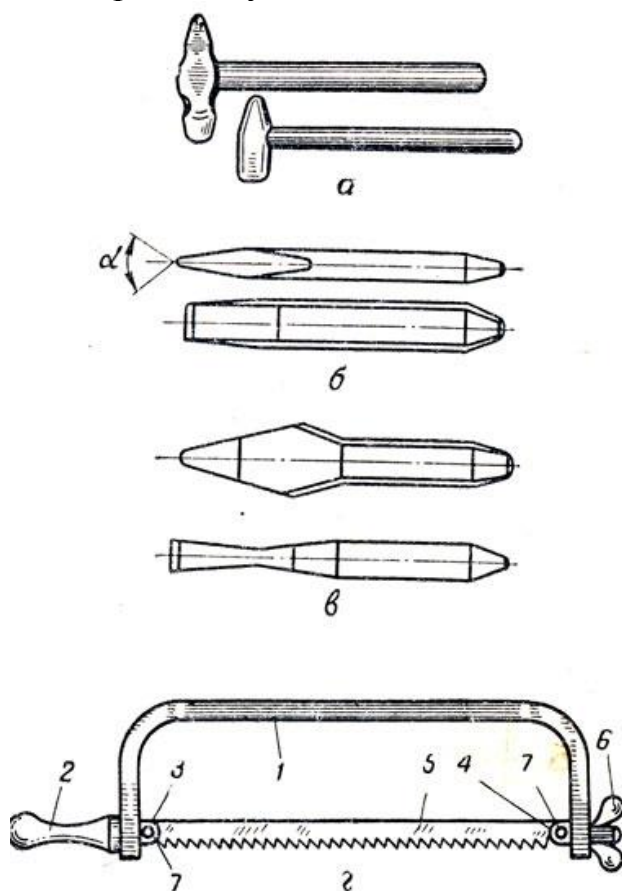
Инструмент для рубки и резки: а - слесарные молотки; б - зубило; в - крейцмейсель; г - ножовка; 1 - рамка; 2 - ручка; 3 - неподвижная головка; 4 - натяжная головка; 5 - ножовочное полотно; 6 - гайка-барашек; 7 - шпилька
